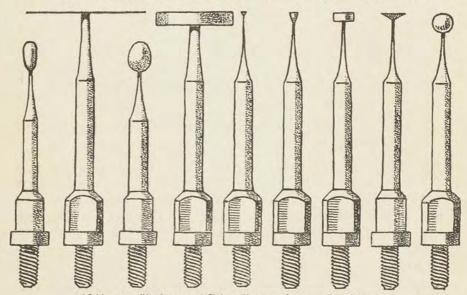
Werkzeuge ("Zeiger") zum Gemmenfcneiden.
